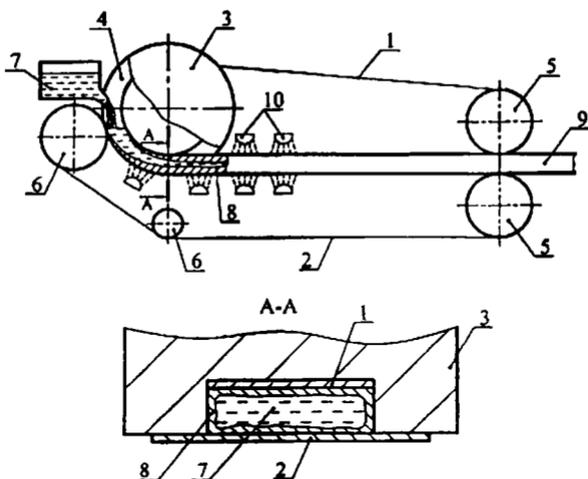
Схема установки непрерывного литья полос: 1, 2 – лента; 3 – барабан; 4 – проточка; 5 – ролик приводной; 6 – ролик натяжной; 7 – расплав; 8 – начальная корка; 9 – отливка; 10 – водяное охлаждение
